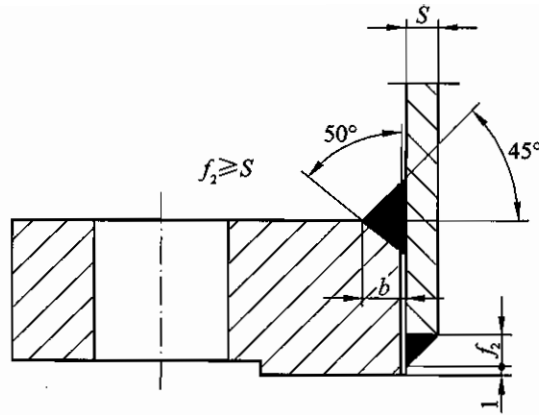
板式平焊法兰或平焊环与钢管连接的焊接接头
